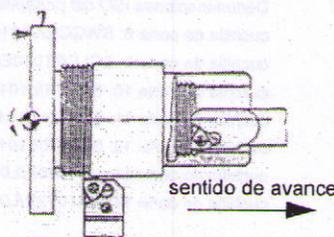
Rosca izquierda en giro derecho del husillo de máquina
